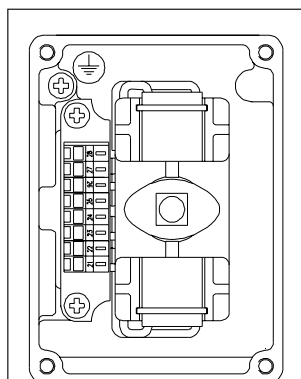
Vista interna dell'interruttore a chiave del pod opzionale
